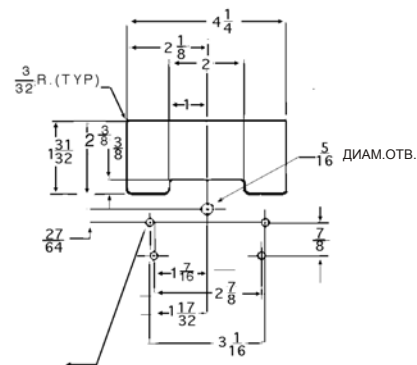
Панельный монтаж (Для приборов без корпуса)
